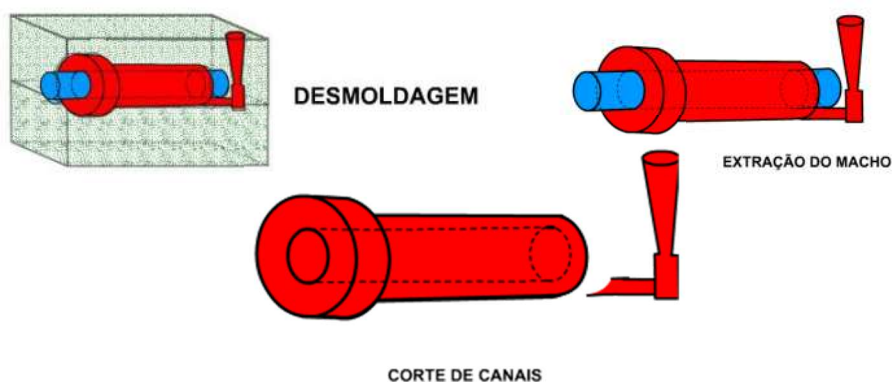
Sequência de desmoldagem, extração do macho e corte de canais de alimentação [6]
